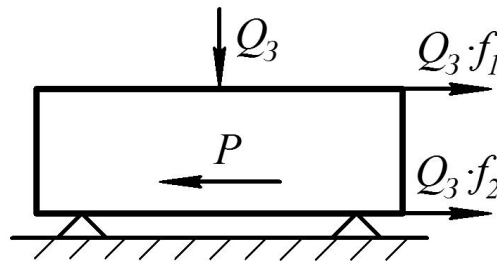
Схема різання для визначення сили закріплення для операцій свердління
